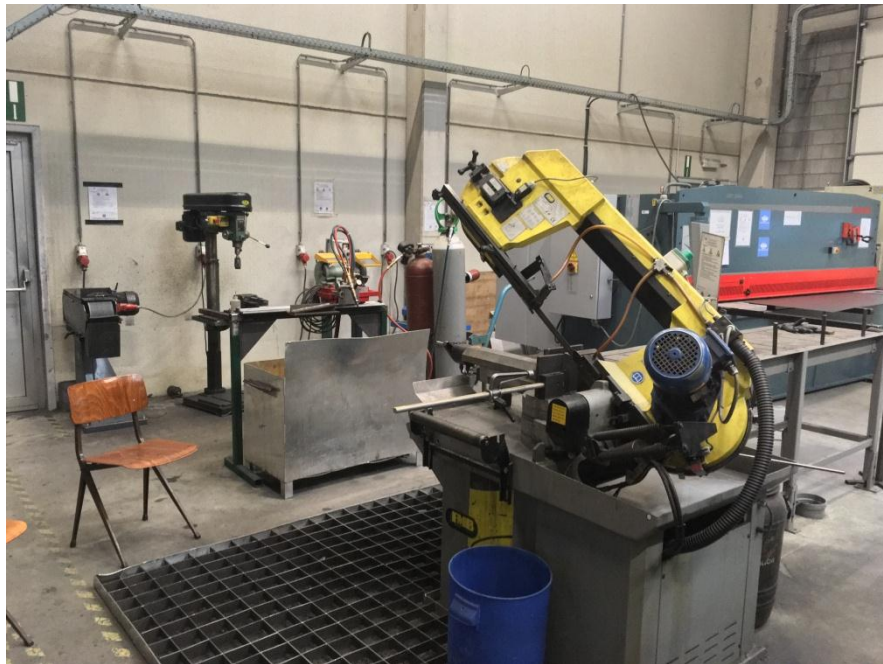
Стрічкова пила FMB SAW*320
